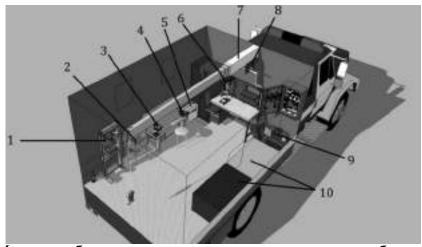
Модель рабочего пространства с расположением оборудования передвижной мастерской. 1— пресс гидравлический, 2 — мойка, 3 — станок заточной, 4 — тиски, 5 — сварочный аппарат, 6 — сверлильный станок, 7 — грузовая стрела, 8 — редуктор, 9 — компрессор, 10 — рундук
